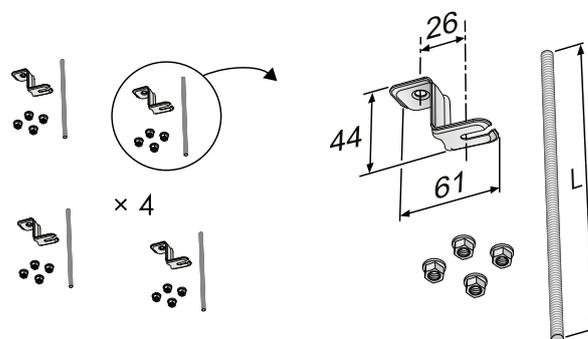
Élément d'assemblage SYST MS M8-1, montage au plafond et sur tige filetée
